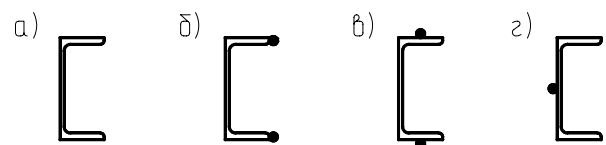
Схема расположения наплавки сварных холостых валиков на швеллерах:
